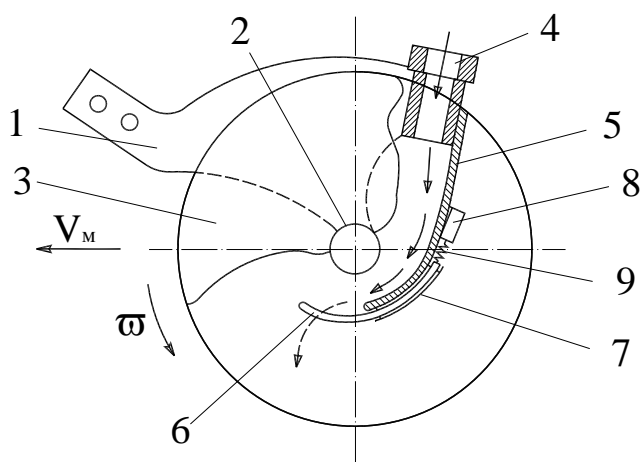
Конструктивна схема розробленого дводискового сошника з мехатронним пристроєм:
